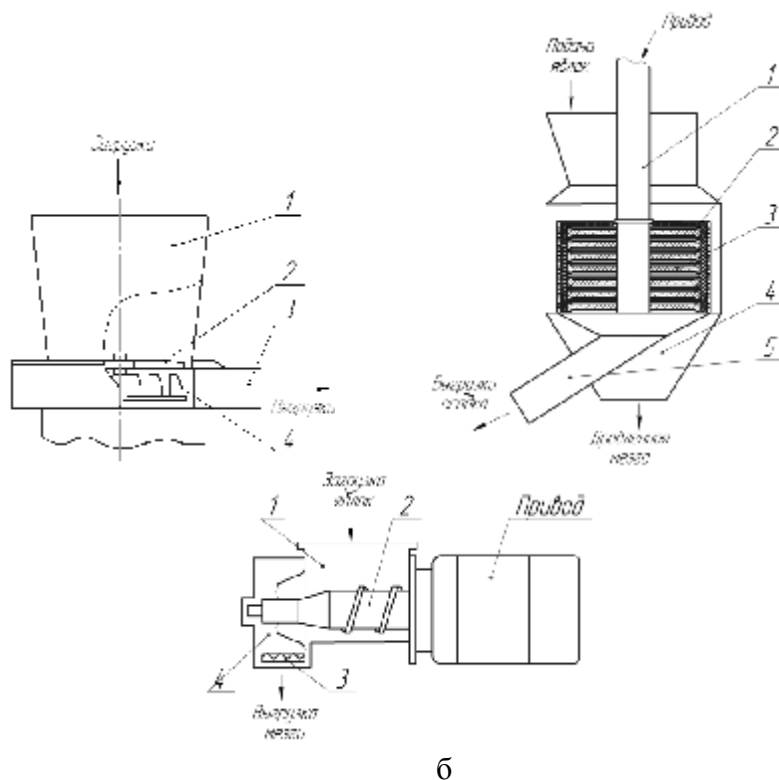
Конструкции машин для измельчения яблок: а – дисковая дробилка ВДР-5; б – молотковая дробилка ЛЕ-6; в – терочная дробилка
